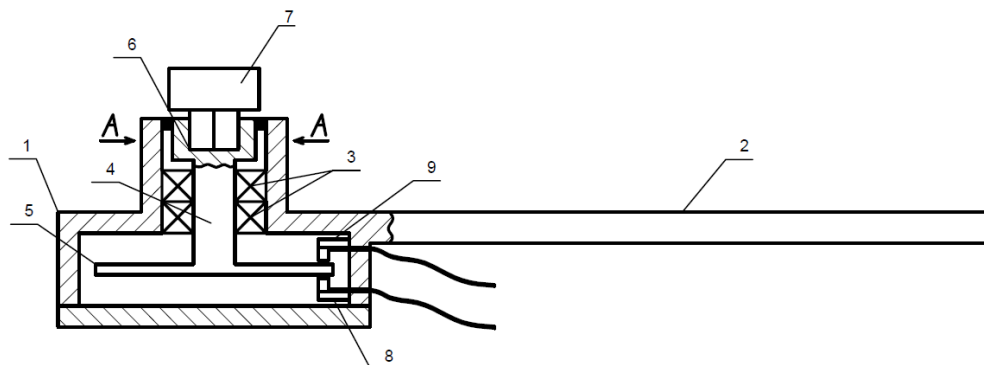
Устройство определения угловой скорости вращения коленчатого вала ДВС: 1- корпус, 2-рукоятка, 3- подшипники, 4-вал, 5-диск, 6-паз, 7-переходник, 8-излучатель, 9- фотодатчик. [36]
